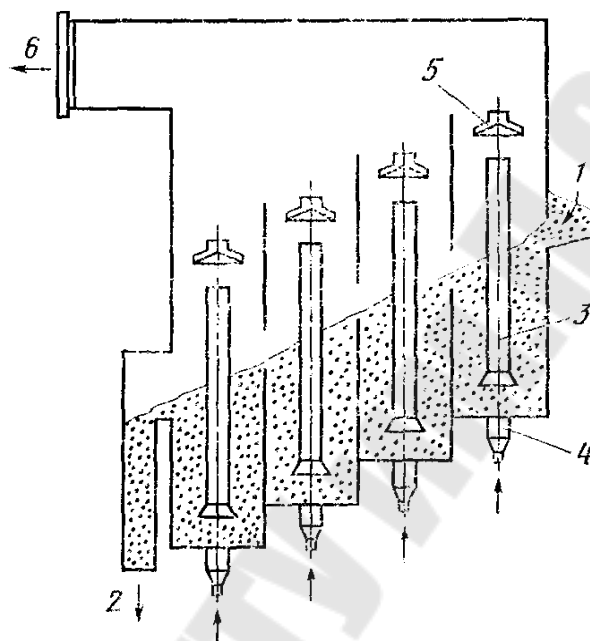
Схема пневматической установки для регенерации: 1- непрерывная загрузка отработанной смеси; 2- непрерывный выпуск регенерата; 3- рабочая труба; 4- подвод сжатого воздуха; 5- колпак; 6- отсос пыльного воздуха
